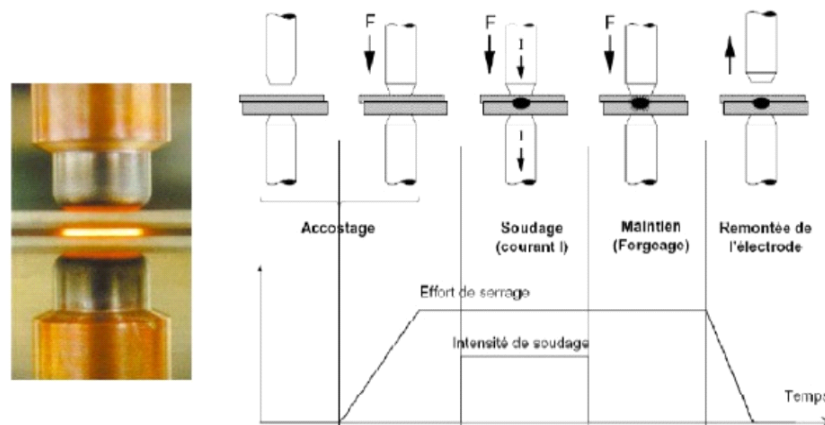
Etapes du procédé lors du soudage par point.
